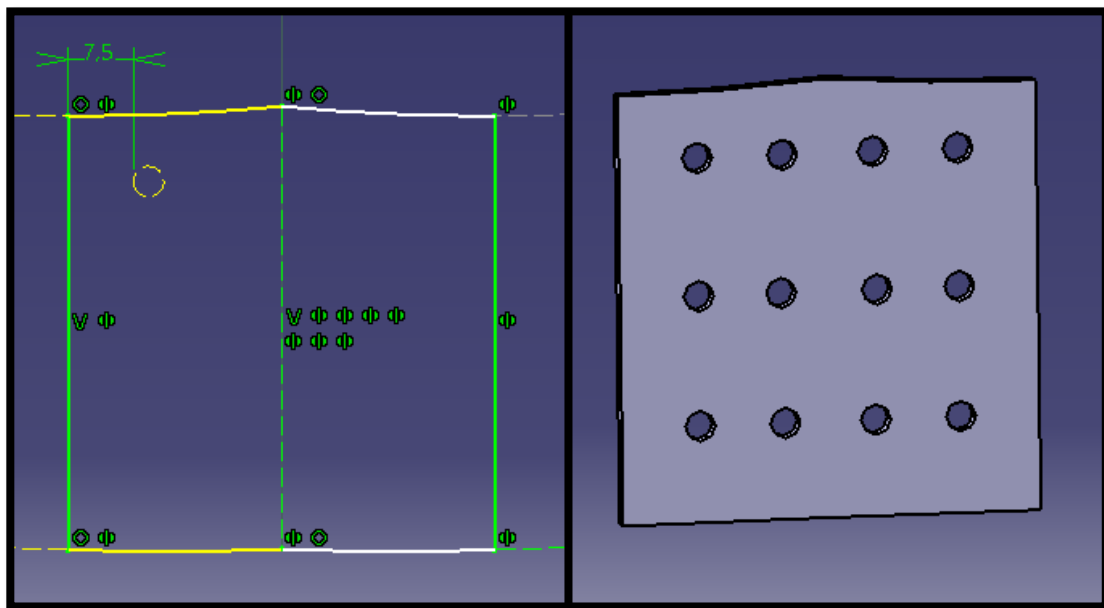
Refuerzo inferior 12: Sketch y pieza final tras extrusión y vaciado
